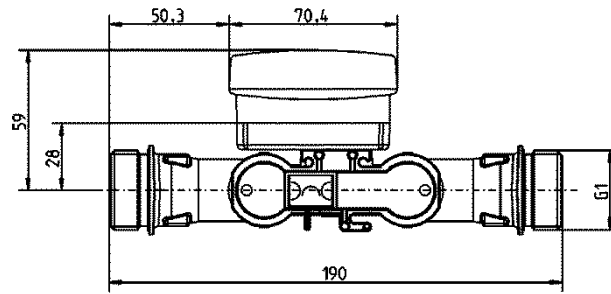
Übersicht Maße Baulänge 190 mm (Gewinde)
